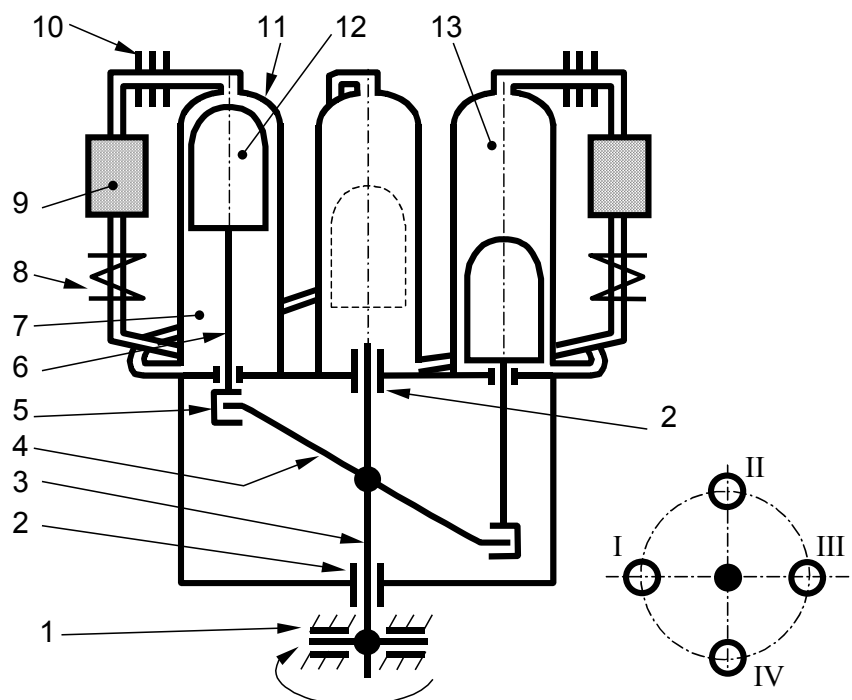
Schema unui motor Stirling cu pistoane cu dublă acțiune cu mecanism cu placă înclinată: 1 - lagăr axial; 2 - lagăr radial; 3 - arbore; 4 - placă înclinată; 5 - falcă dublă; 6 - tija pistonului; 7 - cameră de comprimare; 8 - răcitor; 9 - regeneratoare; 10 - încălzitor; 11 - cilindru; 12 - piston; 13 - cameră de destindere
